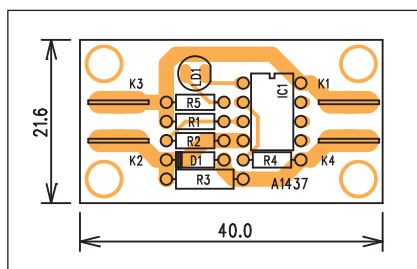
Obrazec desky spojů kapacitního spínače (strana BOTTOM)
